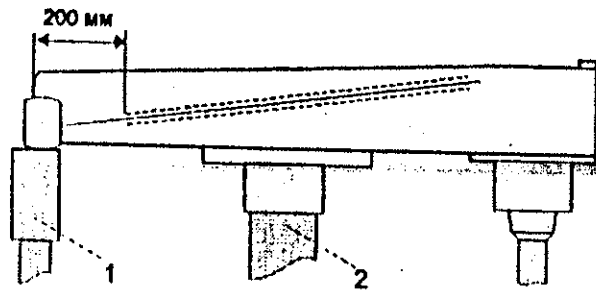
Контроль сварного шва накладок верхнего пояса продольной балки рамы
